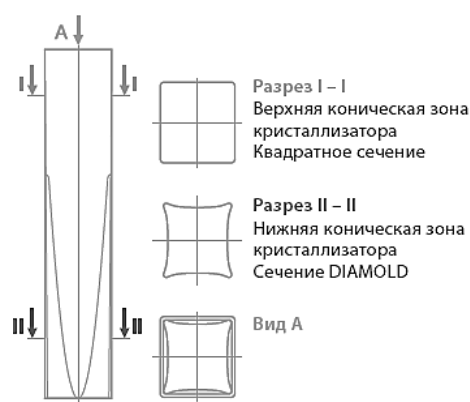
Геометрия кристаллизатора DIA MOULD
